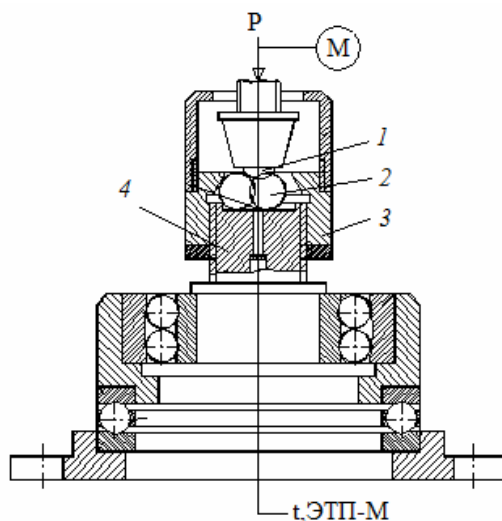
Робочий вузол установки для чотирикулькової схеми
